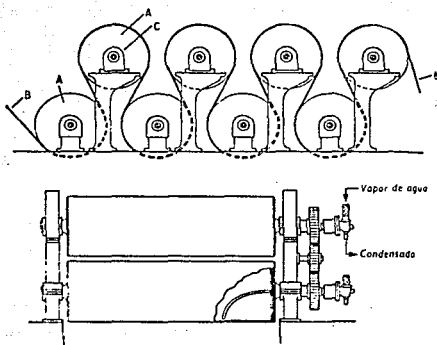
FIG. VI-VI .- SECADOR DE CILINDROS., A, cilindros;
